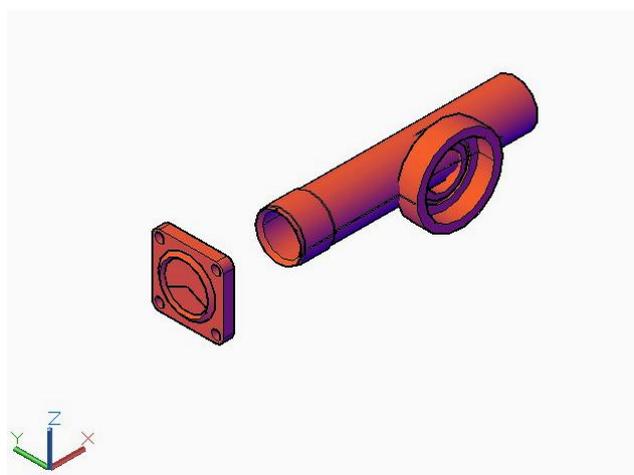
Результат 3-D поворота детали 8б относительно детали 8а.
